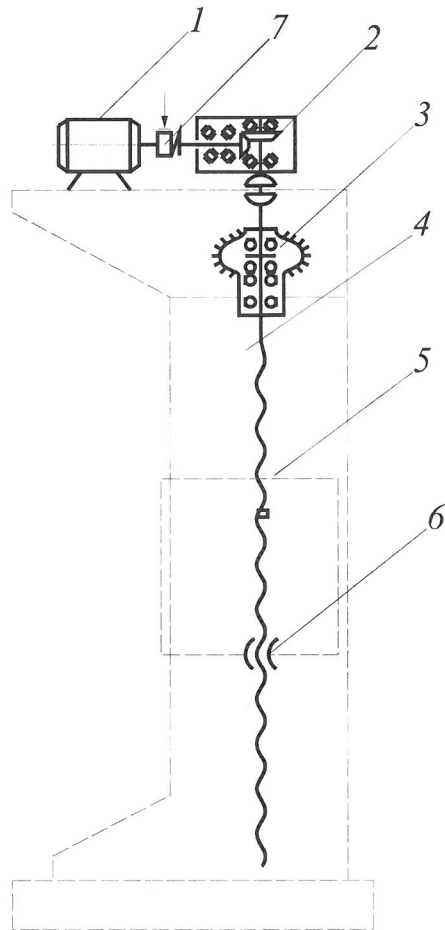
Кінематична схема піднімального привода: 1 - електродвигун; 2 – конічний редуктор; 3 – корпус опорних підшипників; 4 – підйомний гвинт; 5 – рухомий візок; 6 – ходова гайка; 7 – муфта з гальмом.
